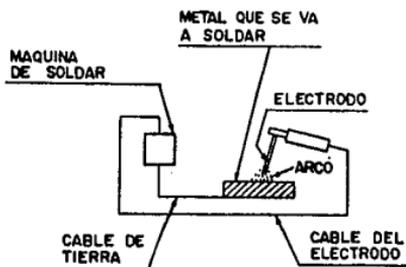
Circuito de Soldadura de Arco.
